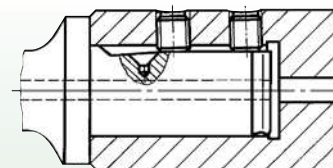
Хвостовик сверла по DIN 6595/ISO 9766 и крепление с помощью двух винтов с плоским торцем.
